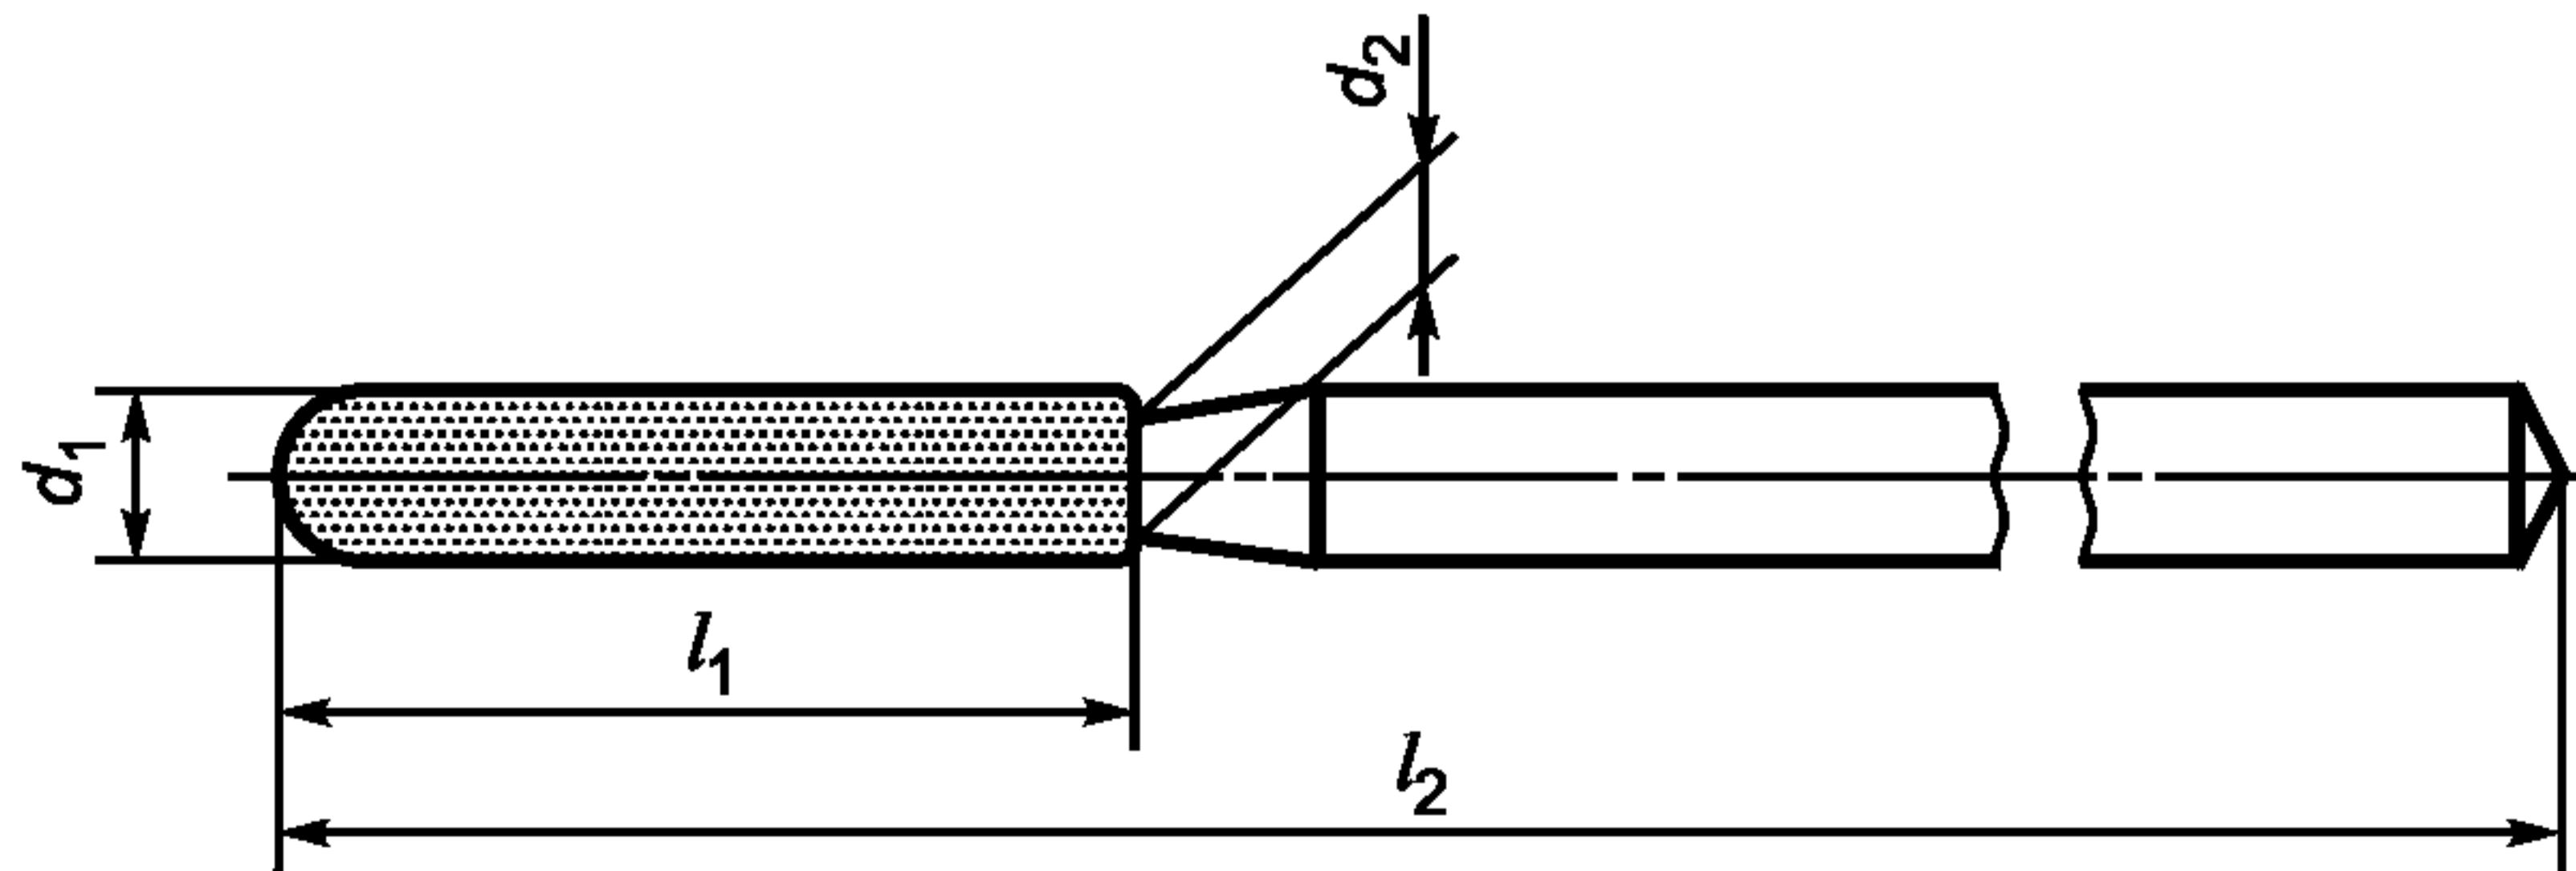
Цилиндрическая полусферическая рабочая часть с длиной головки 10,0 мм
